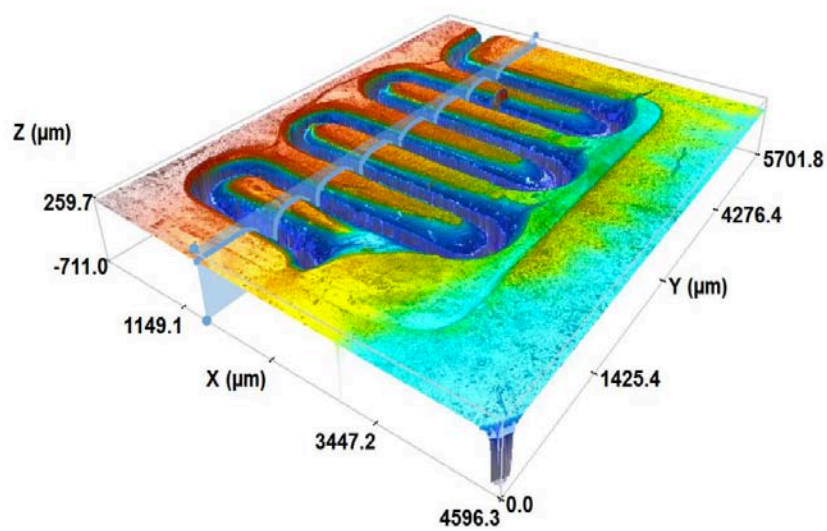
Serpentina – Componente stampato da inserto fresato - D
